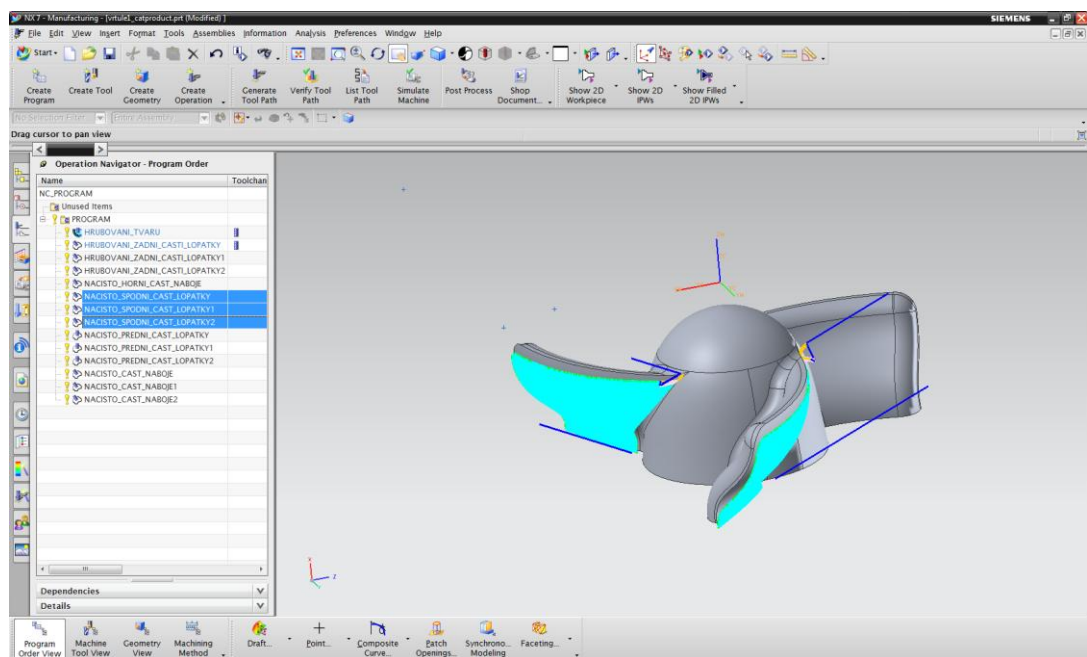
Operace načisto horní část náboje Vrtule1 (Siemens NX7.5)
